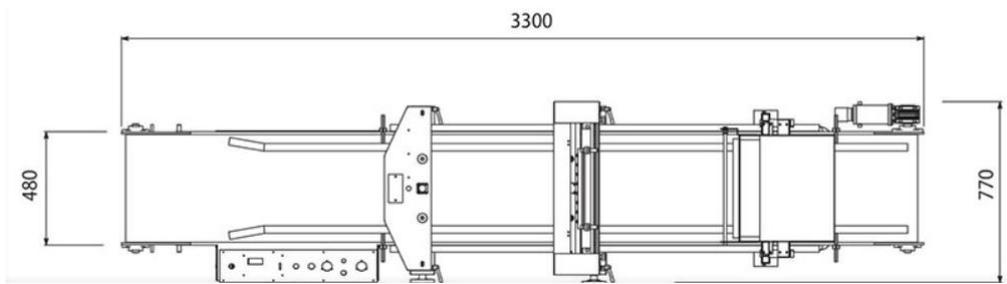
Máquina germinadora. Fuente: Empresa proveedora.
